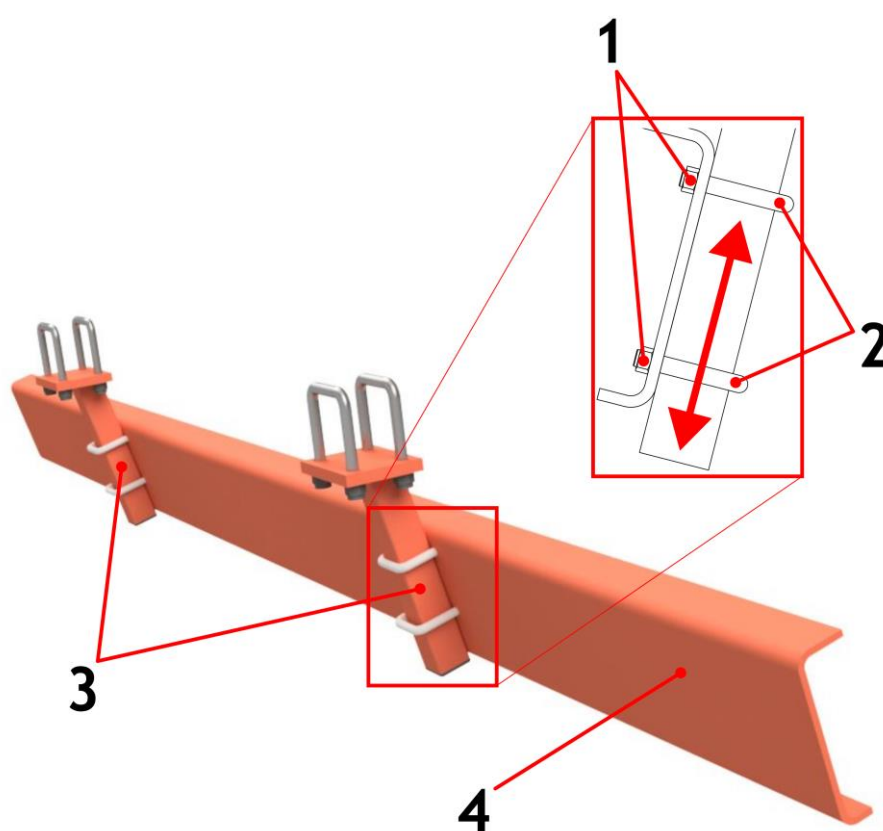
Réglage de la position de l'écran central et sa construction (1 - écrous de fixation, 2 - colliers de serrage, 3 - supports de l'écran montés sur la structure du châssis, 4 - écran central).
